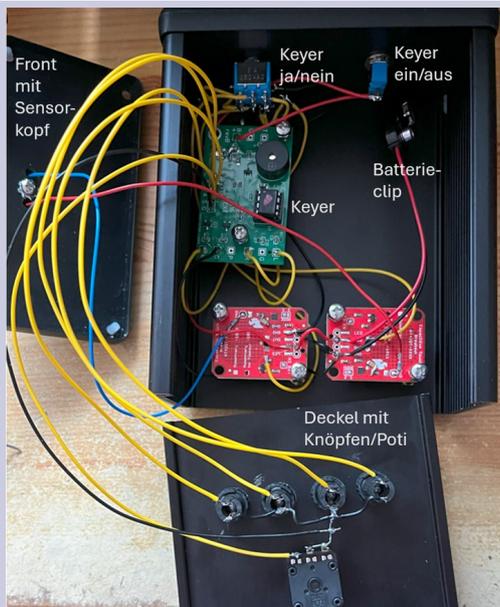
Innenansicht der kompletten Taste mit Anschlüssen
